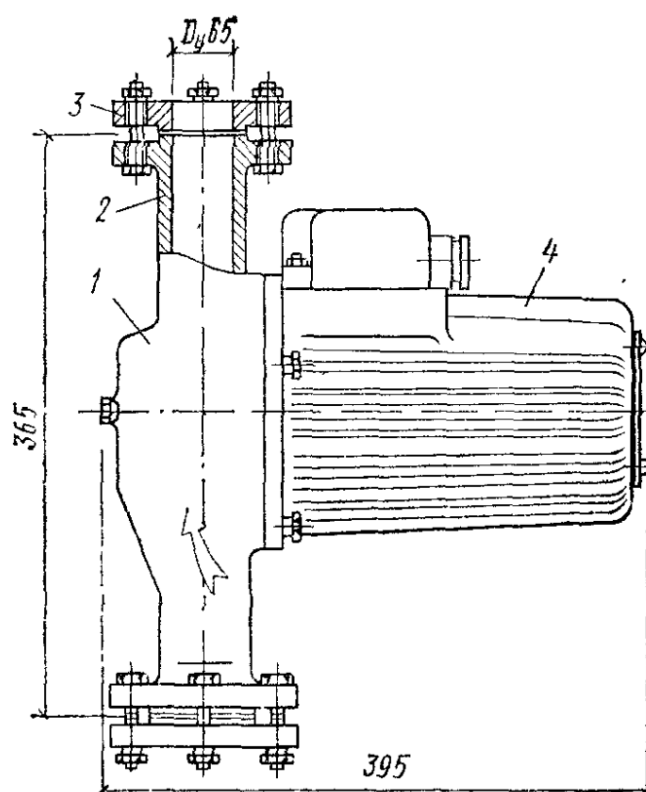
Центробежный циркуляционный насос: 1 – корпус; 2 – нагнетательный патрубок; 3 – контрольный фланец для присоединения трубы; 4 – электродвигатель
